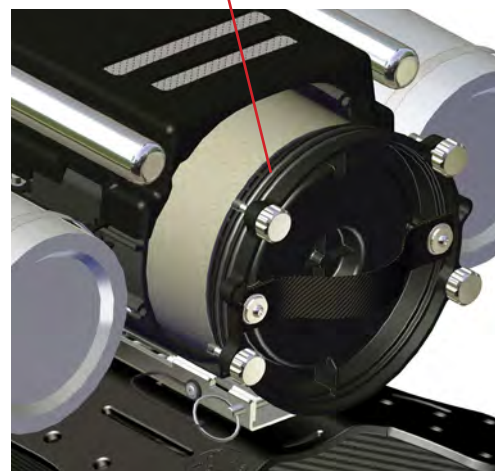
Skjut in bottenplattan med o-ringar i aluminiumröret.
